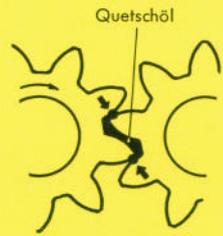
Quetschöl in den Zahnücken einer Zahnradpumpe (die kurzen Pfeile zeigen auf die abdichtenden Stellen)
